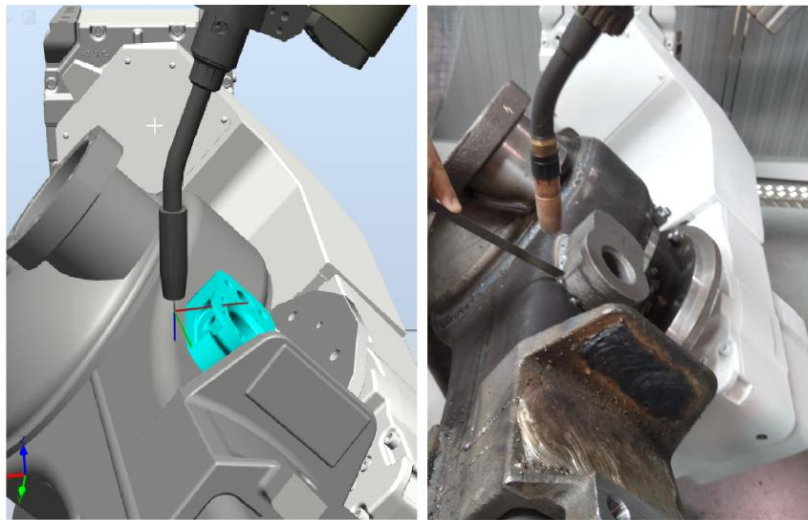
Teste virtual e real de soldadura com eixo suportado em posicionador
